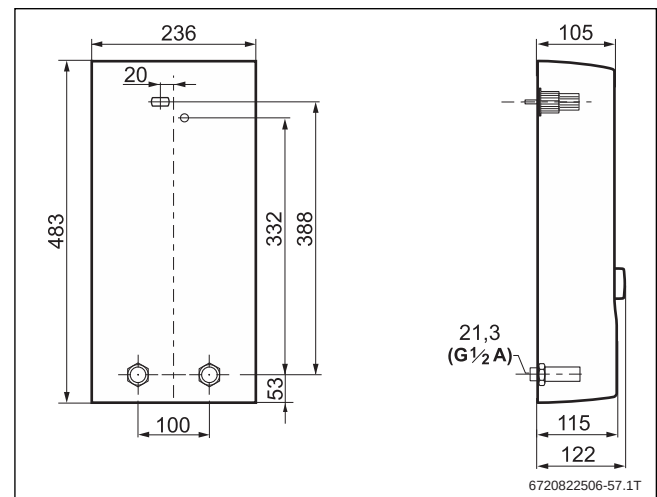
Abmessungen Tronic 7000 DESOB (Maße in mm)
